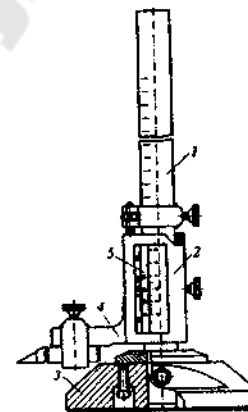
Штангенрейсмас: 1 – штанга-линейка; 2 рамка; 3 – основание; 4 – державка; 5 – нониус
